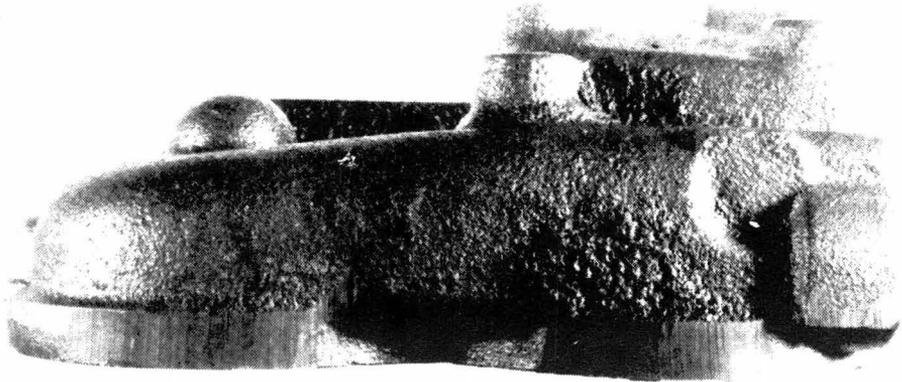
Mal apisonado del molde ocasiona este defecto.
